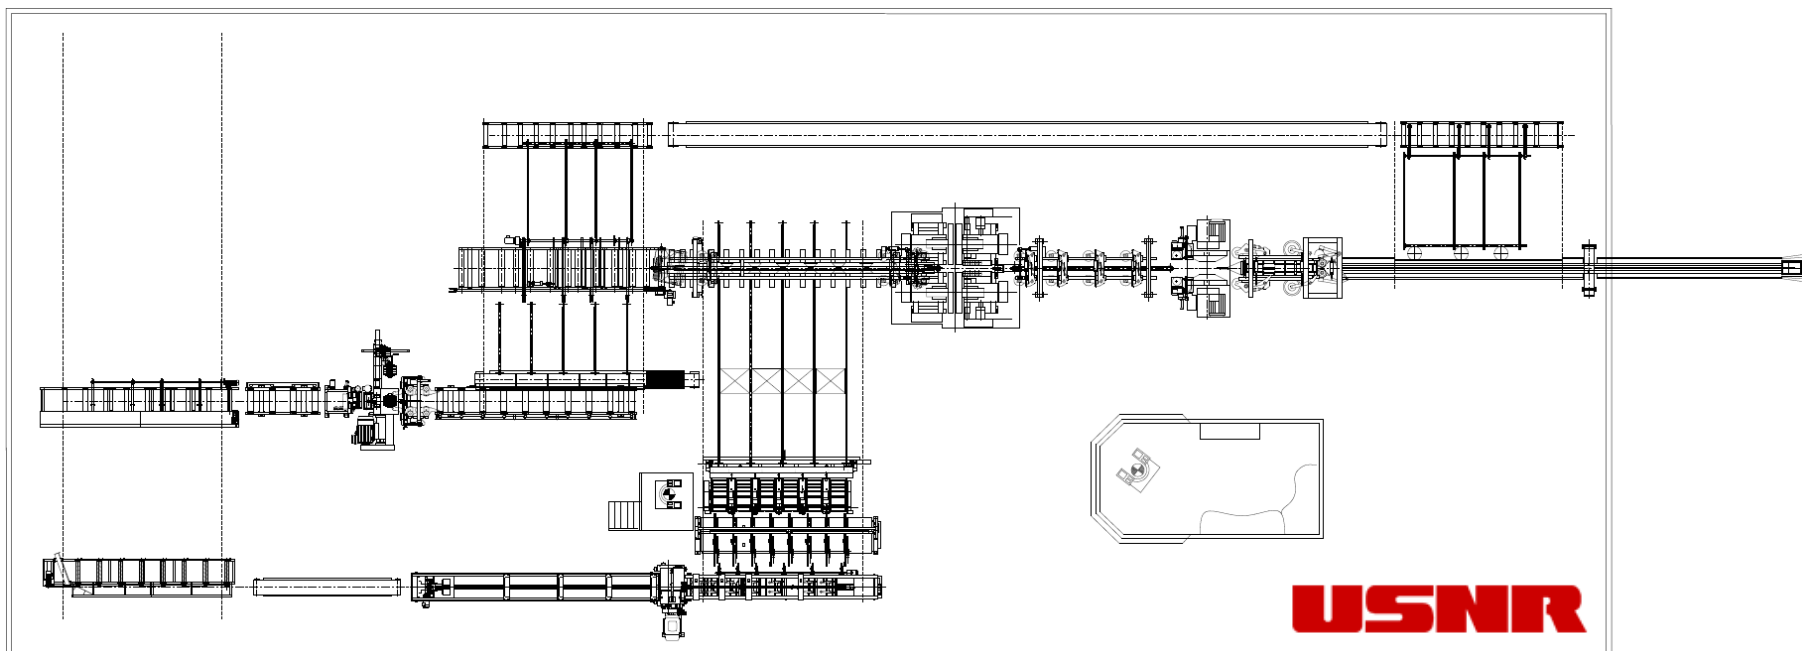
Лесопильная линия на базе фрезерно-ленточнопильного оборудования и делительного станка для бруса [10]
